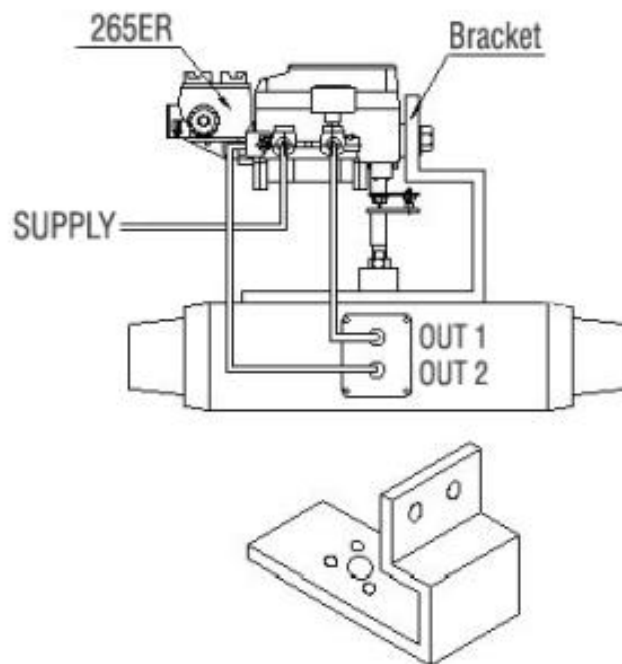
Схематичне креслення пневматичної системи керування.
